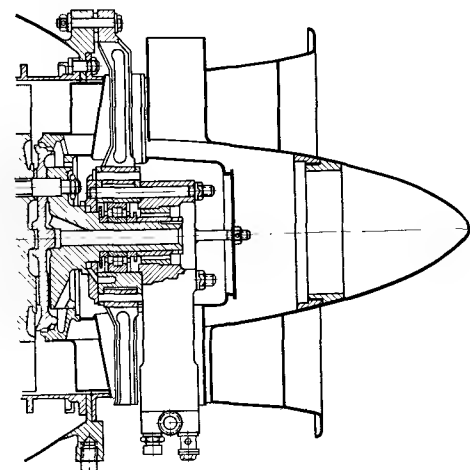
Крепление корпуса подшипника ГТУ «Артуст» фирмы Турбомека
